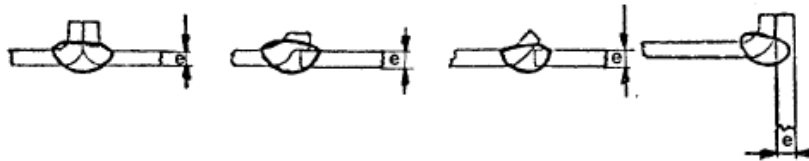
Tipo de contorno en soldaduras a tope con canto levantado [13]
